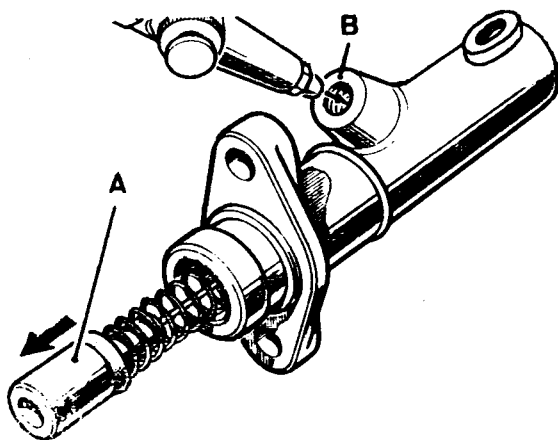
9 - Desmontaje del émbolo del cilindro principal.
